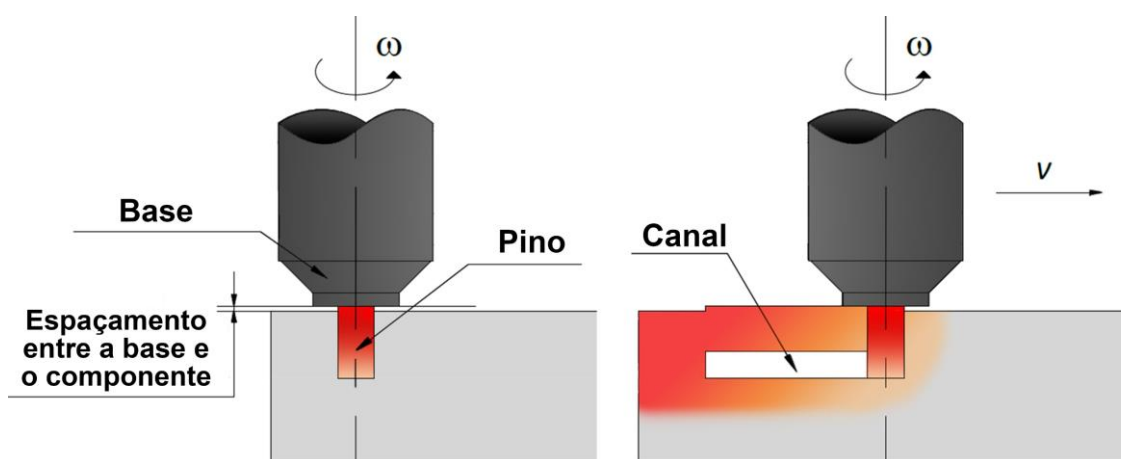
Esquematização da técnica *FSC with Clearance*, adaptado de [2].
